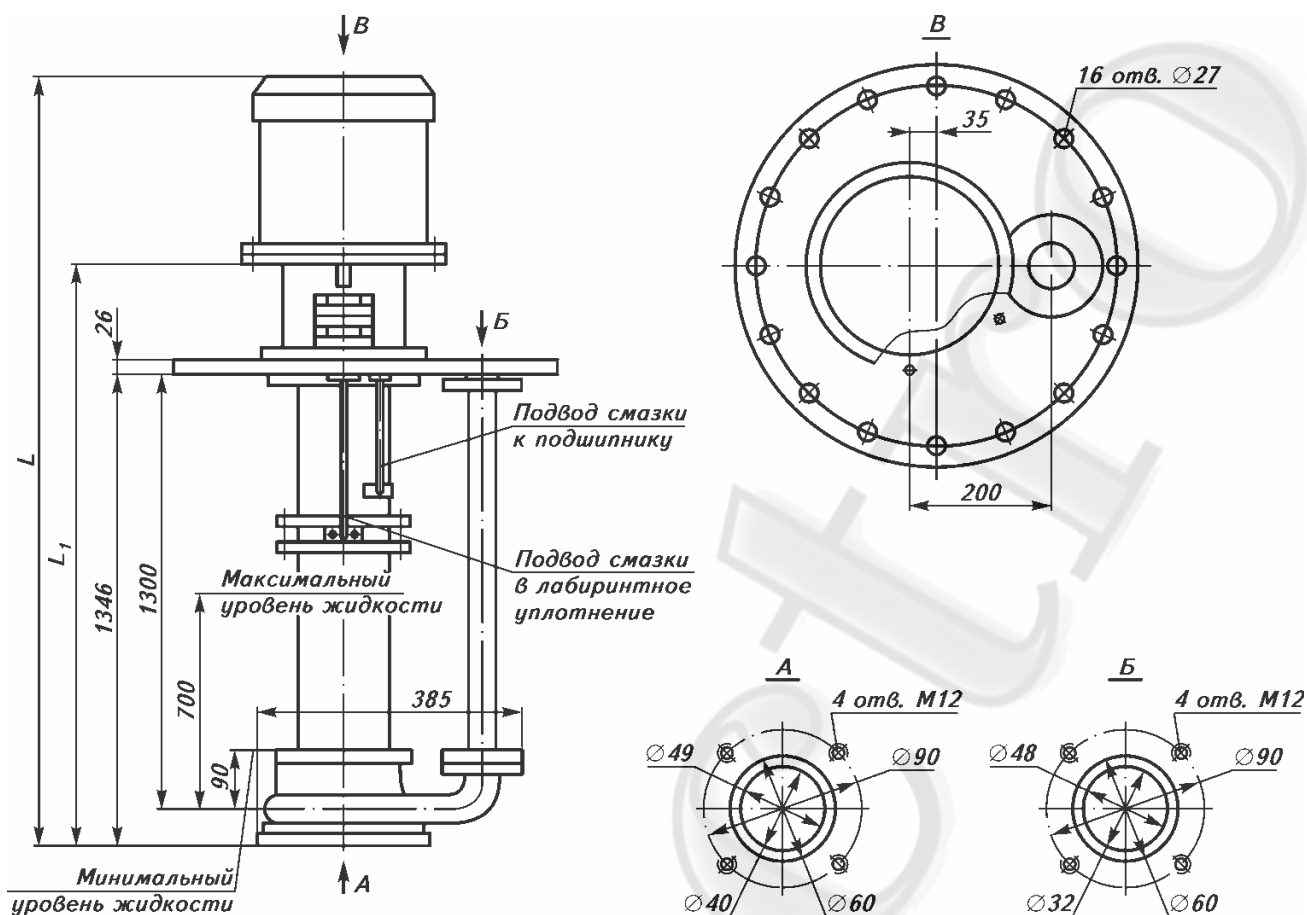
Общий вид, габаритные, присоединительные размеры и масса агрегатов при комплектации электродвигателями различных типов
